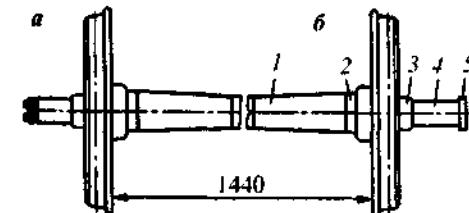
Колесная пара для вагонов с роликовыми подшипниками (а) и с подшипниками скольжения (б): 1 — средняя часть; 2 — подступичная часть; 3 — предподступичная часть; 4 — шейка оси; 5 — бурт
